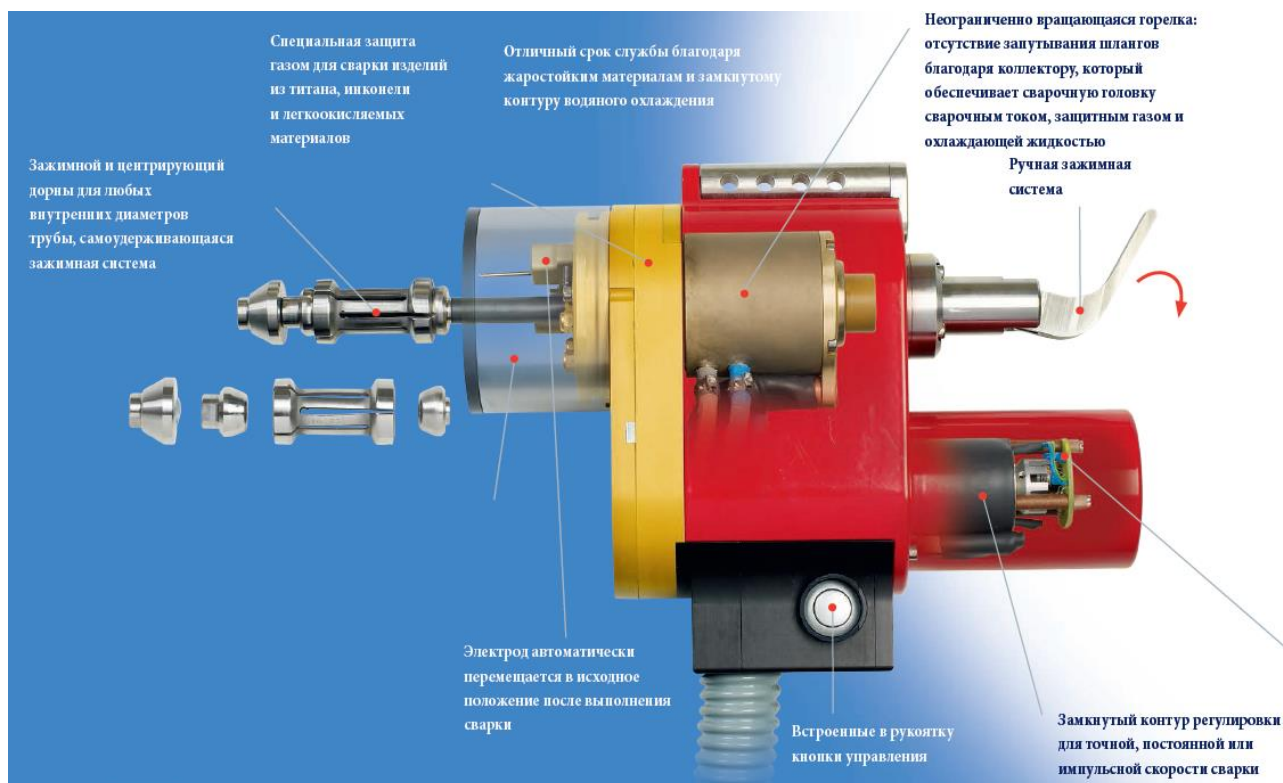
Сварочная головка «POLYSOUD» TS34
